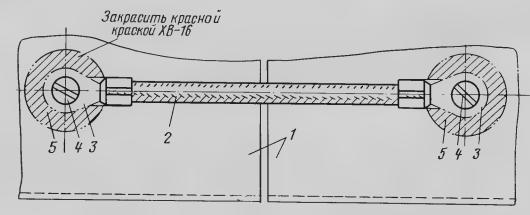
Типовая маркировка перемычки металлизации: 1 — детали конструкции; 2 — перемычки металлизации; 3 — наконечник; 4 — болт; 5 — очищаемая поверхность d=25 мм
